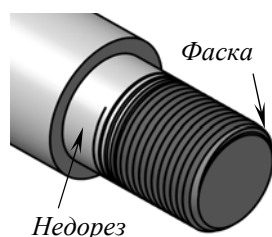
Недорез* резьбы при выполнении резьбы на ступени вала в упор
